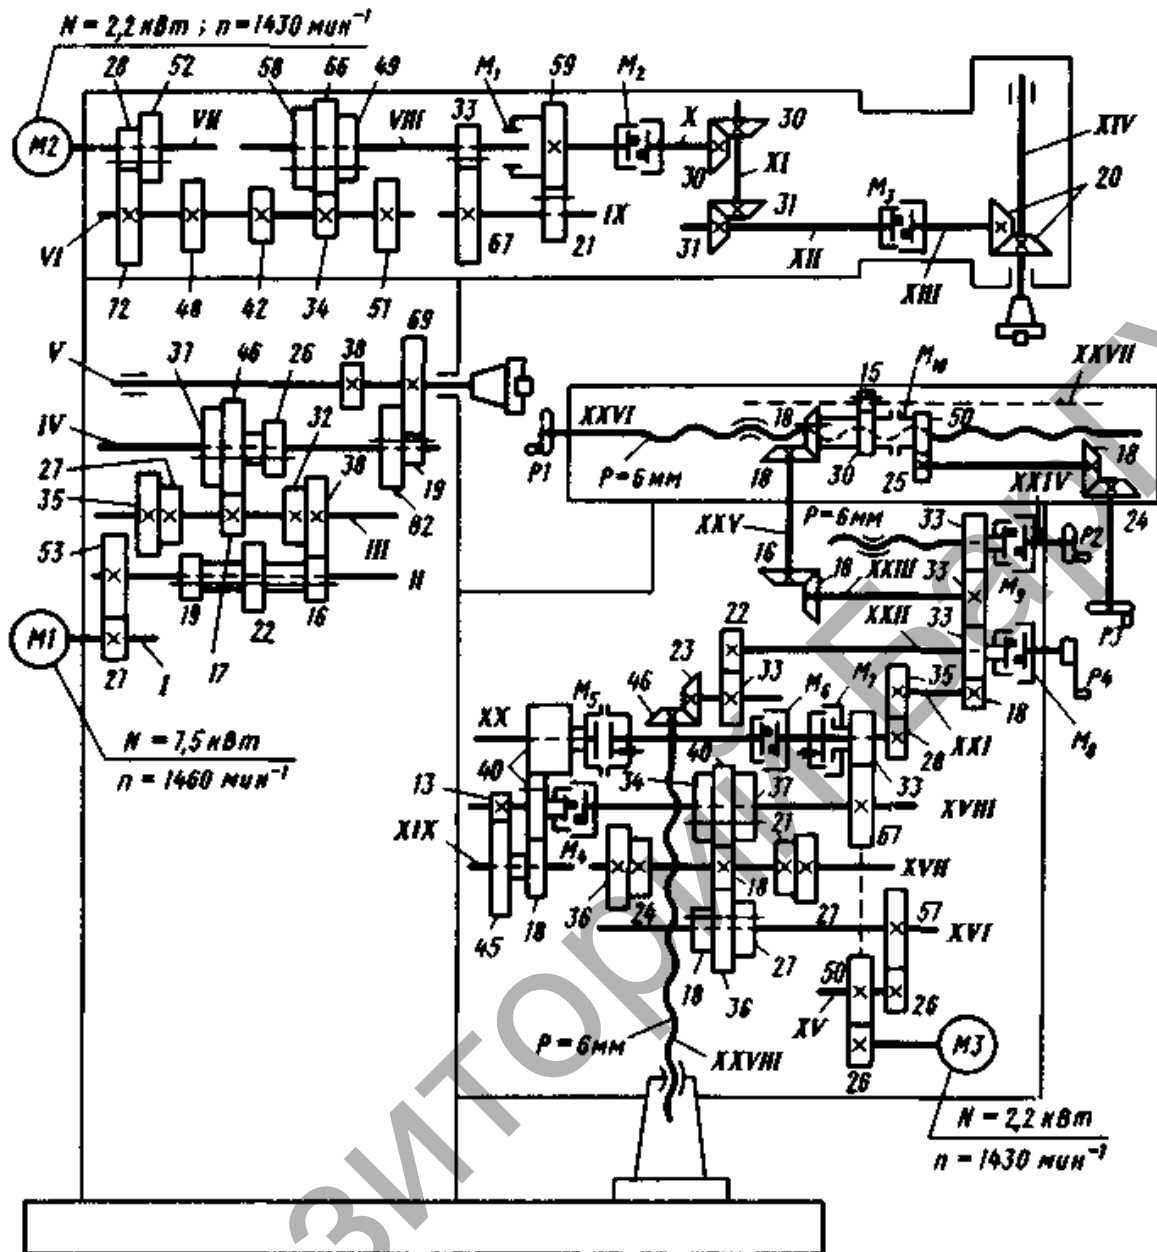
Кинематическая схема станка модели 6P82Ш
